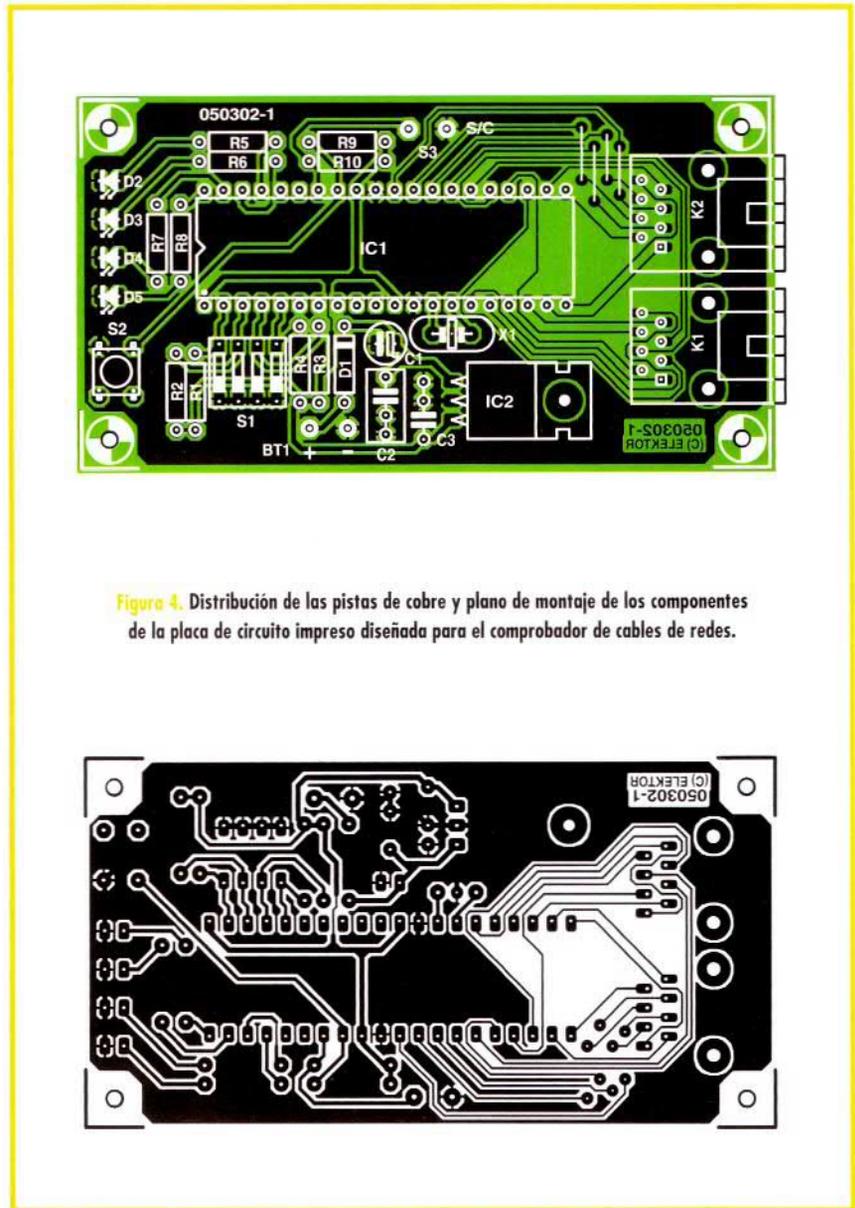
Distribución de las pistas de cobre y plano de montaje de los componentes de la placa de circuito impreso diseñada para el comprobador de cables de redes.
